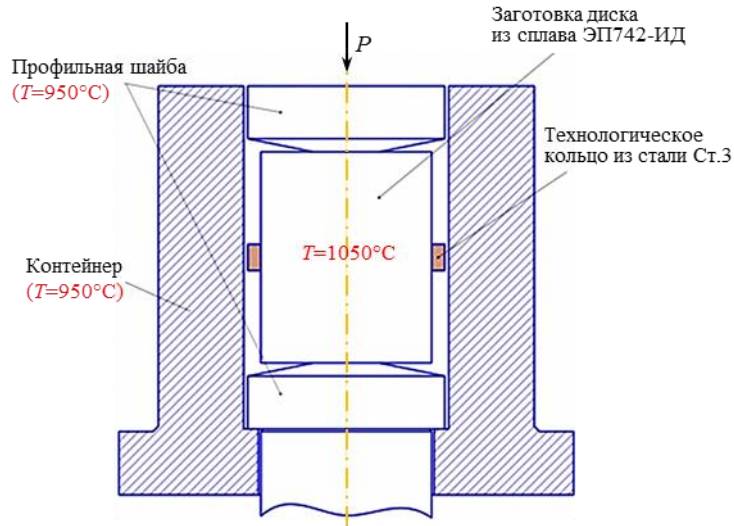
Схема деформации заготовки диска в закрытом контейнере с профильными пресс-шайбами
